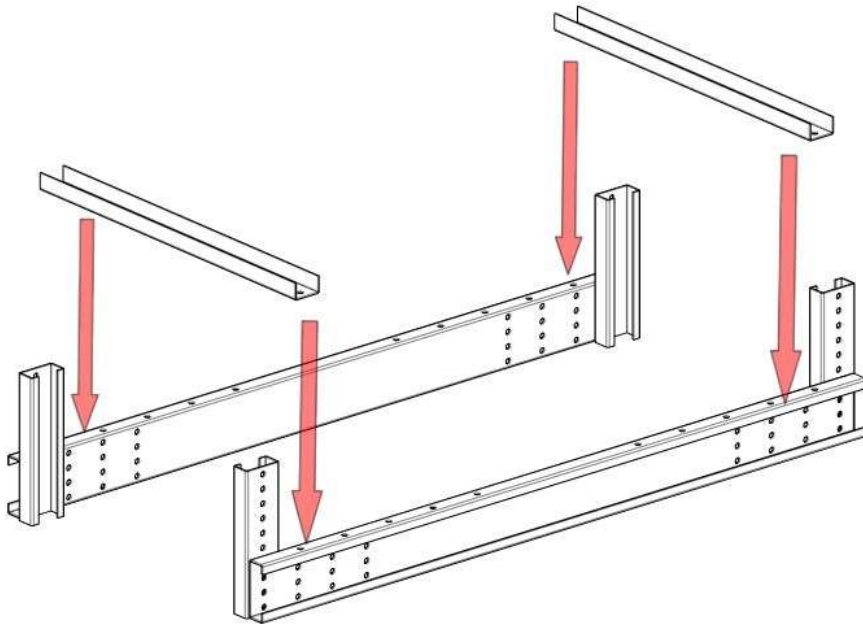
LOWER SECTION ASSEMBLY
